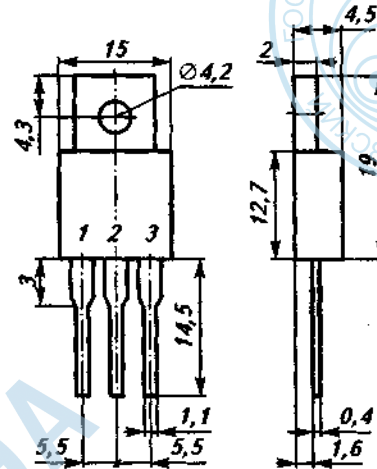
Общий вид, габаритные и присоединительные размеры транзистора КТ8111А в корпусе КТ-43:
